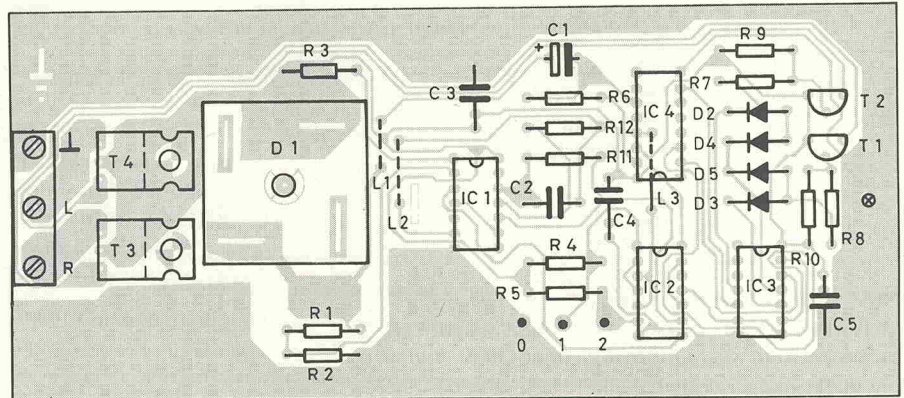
T3, T4 sowie die Brückengleichrichter werden an ein gemeinsames Kühlprofil geschraubt.
